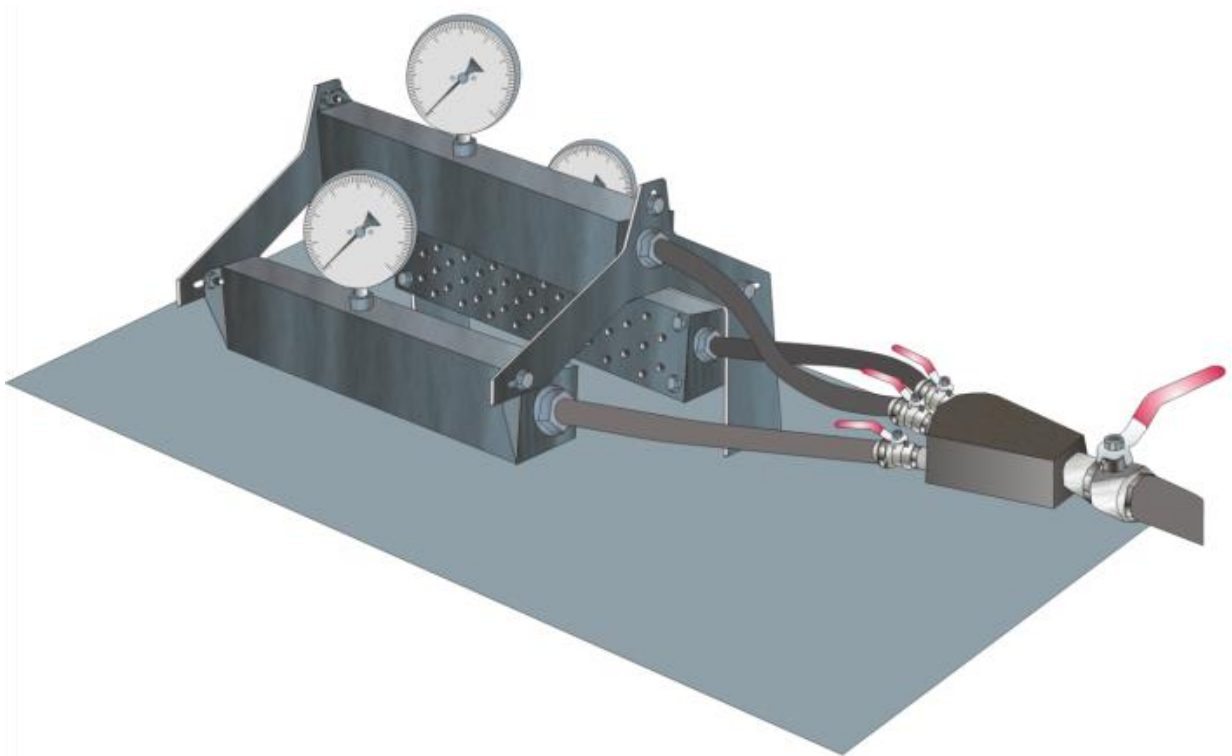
Внешний вид опытной установки для воздушоструйной дифференцированной термической обработки рельсовых проб
